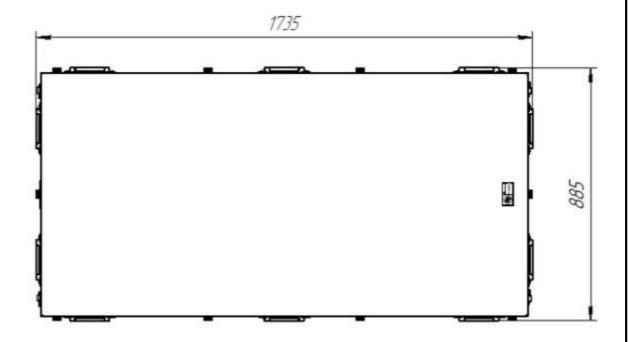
Габаритные размеры ЗССС 1,2 м (вид в транспортном положении)
